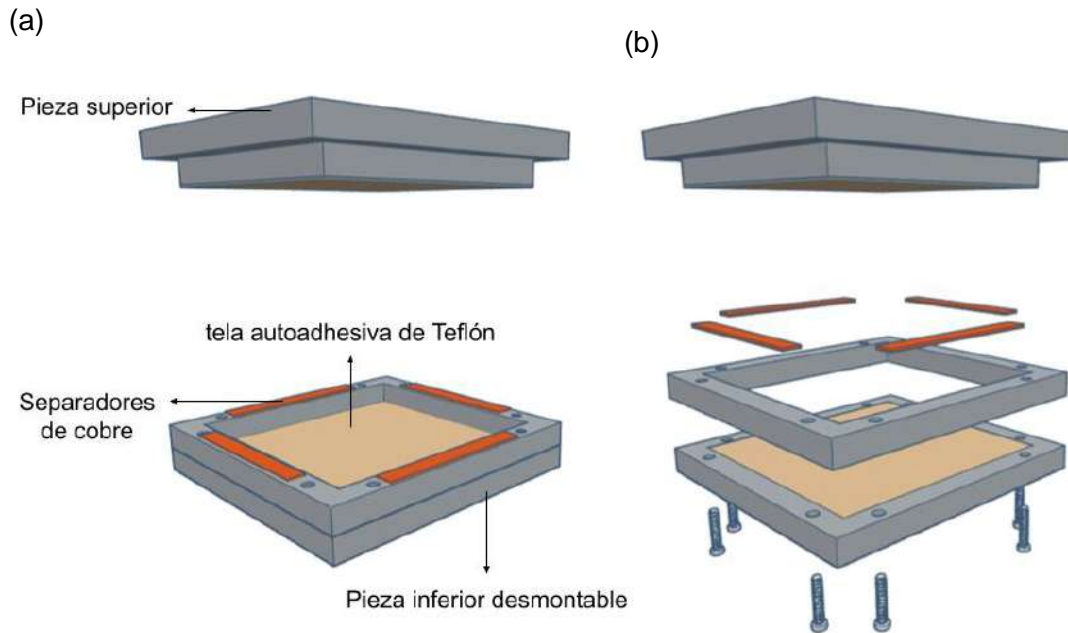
(a) Esquema del molde utilizado para obtener placas de material compuesto y (b) despiece.
